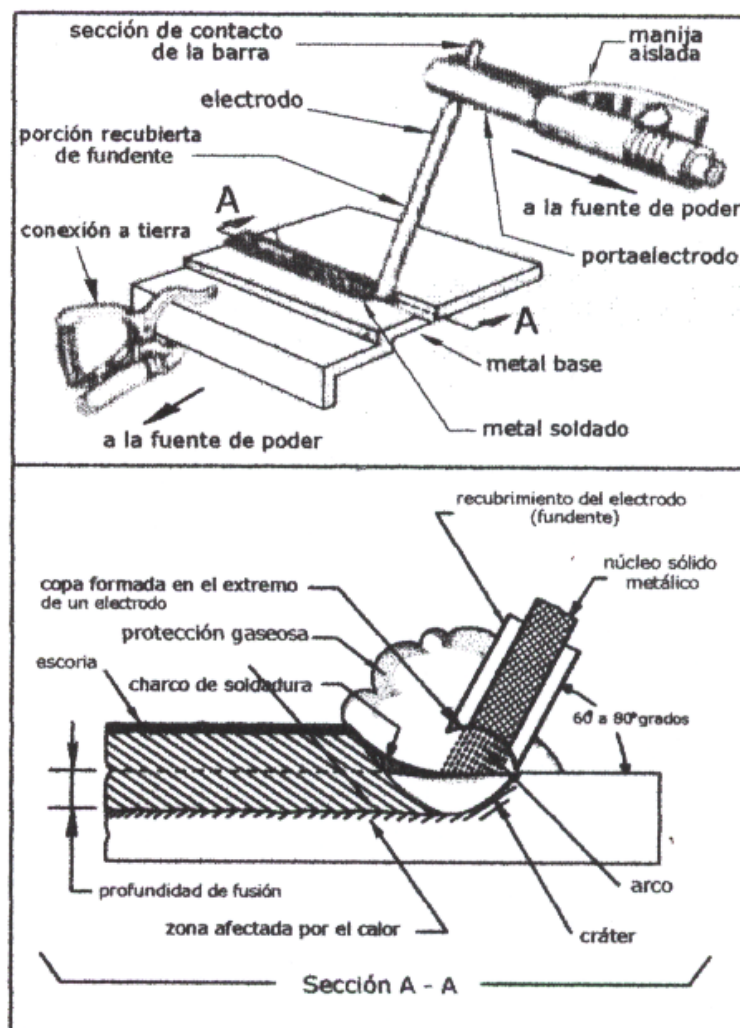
FORMACIÓN DE UN CORDÓN DE SOLDADURA SMAW (1)
